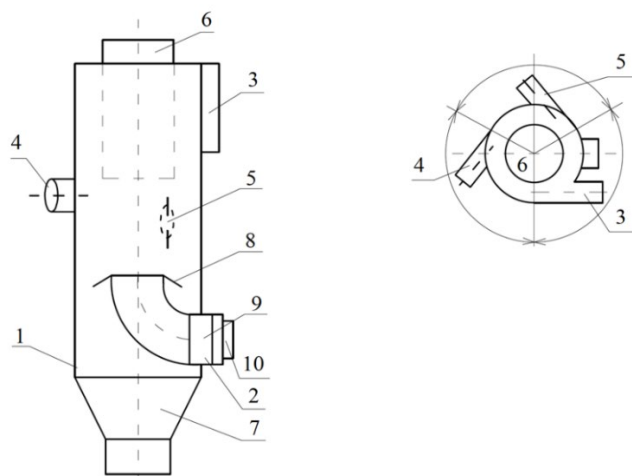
Схема коллектора-пылеуловителя КП-ВЗП: 1 — корпус; 2 — ввод вторичного запыленного потока; 3, 4, 5 — вводы первичного запыленного потока; 6 — патрубок вывода очищенного воздуха; 7 — пылесборник; 8 — отбойная шайба; 9 — завихритель; 10 — люк для прочистки [10]
